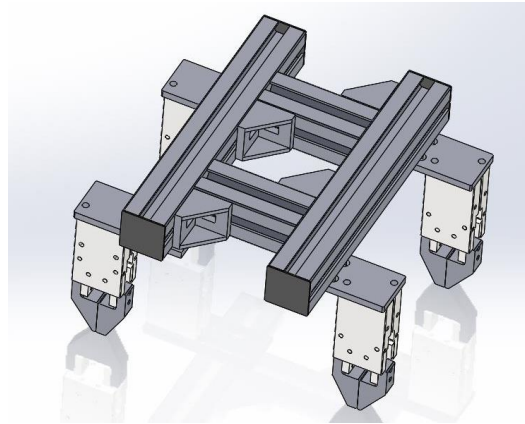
Pinzas de extracción empleadas para este proyecto
